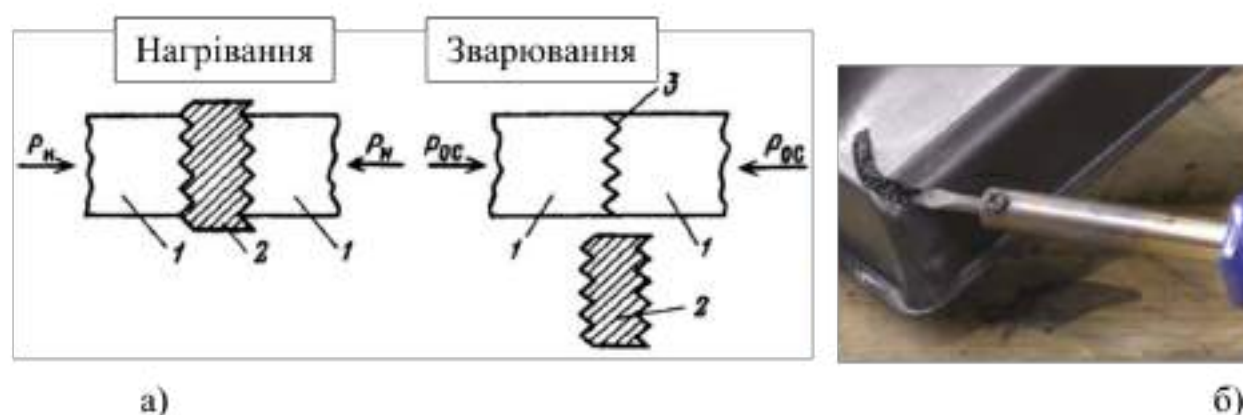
Схема зварювання нагрітим інструментом (а) та відновлена деталь (б): 1 - деталі, що з'єднуються; 2 – інструмент; 3 – шов
